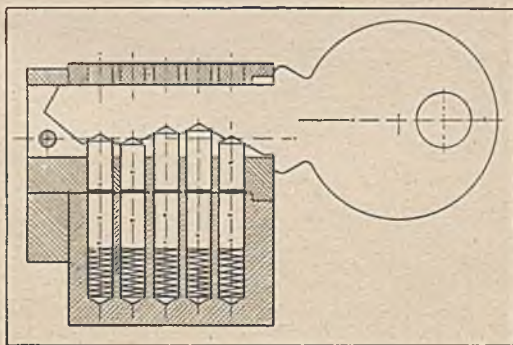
Schloßquerschnitt mit eingeführtem Schlüssel
